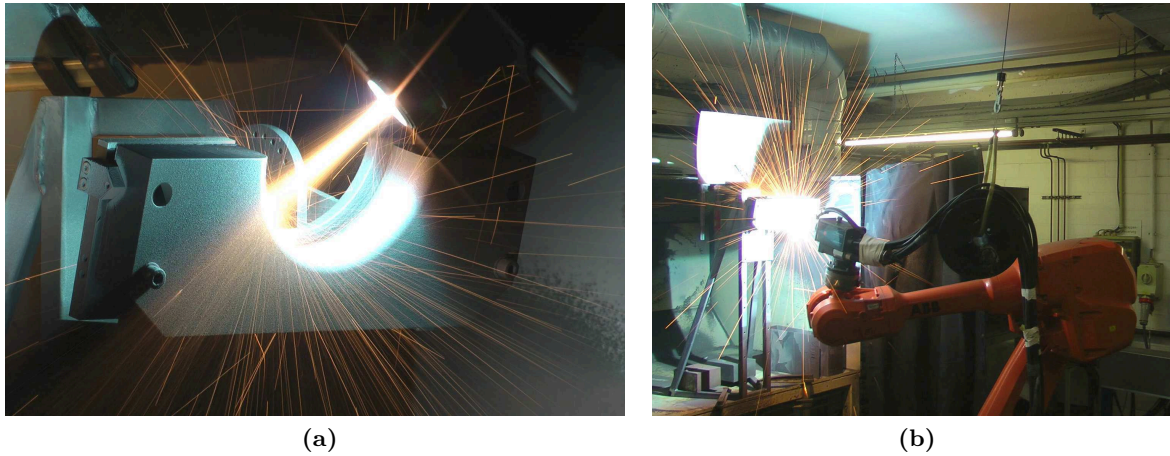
Beschichtung des Bauteils MAT3D mit dem Lichtbogensspritzprozess. (a) Detailansicht der mit nach oben weisendem Radiusausschnitt in der Halterung montierten Probe im Beschichtungsprozess. (b) Stellung des Roboters mit Führung des Schlauchpakets über eine mit einem Federzug an der Decke aufgehängte Rolle.
